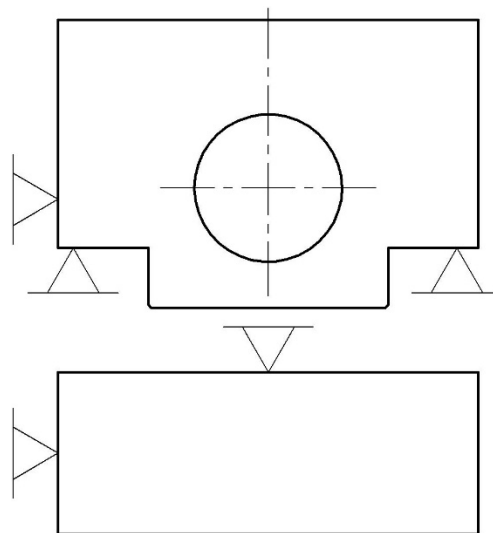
Схема установки заготовки на тактовому столі
